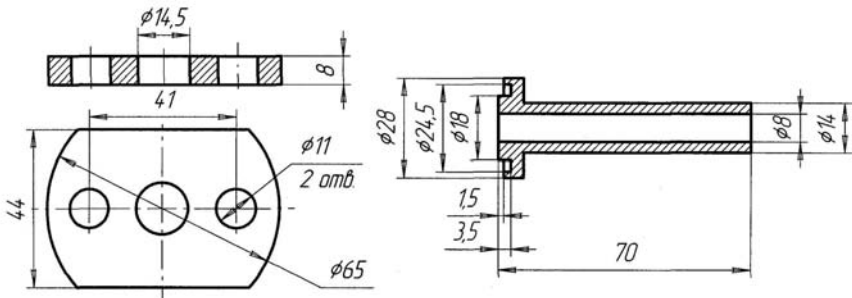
Вварной ниппель для преобразователя ЗОНД-10-ДД.
